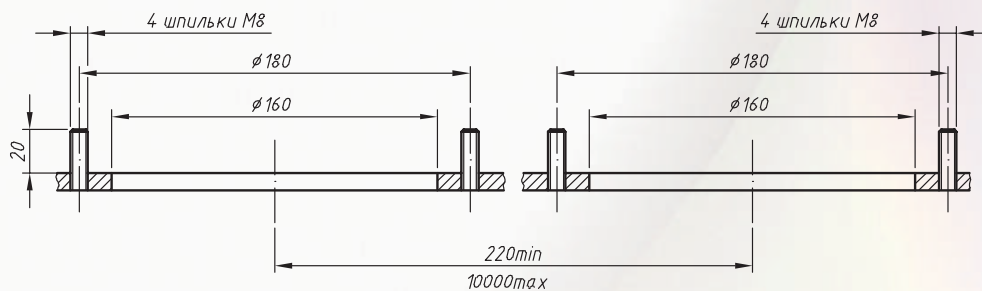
Эскиз доработки крышки резервуара для установки ППП1 (НБ/АПЖ)
